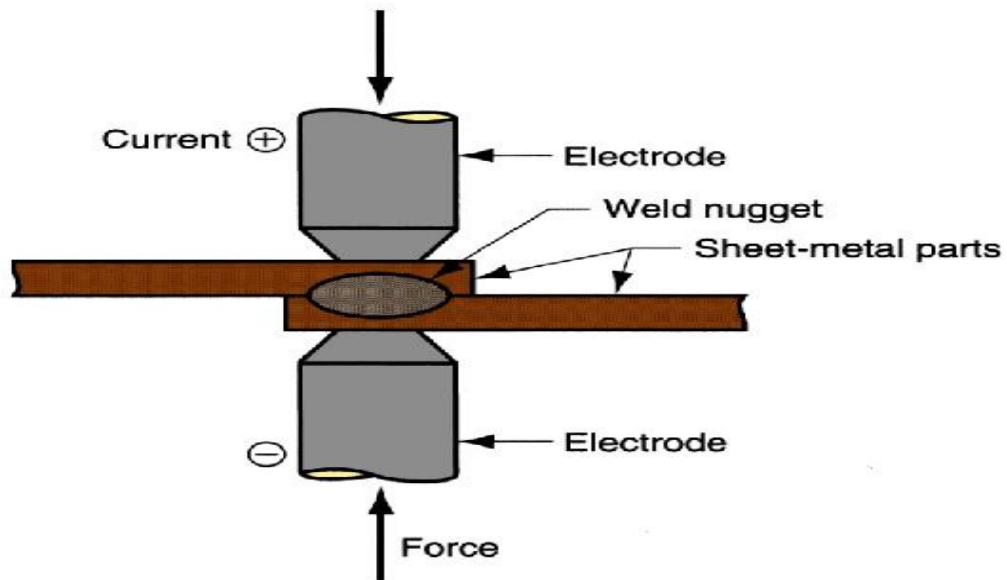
Formação do ponto de solda. (Laprosolda.ABS)
